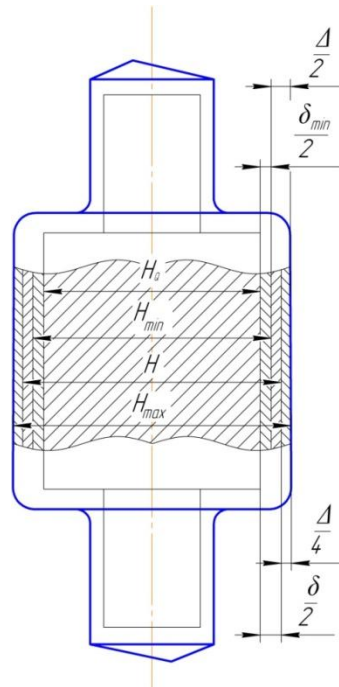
Схема расположения припусков и допусков на наружный размер детали
